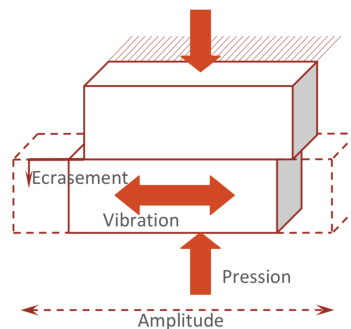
Principe du soudage par friction linéaire [46]
